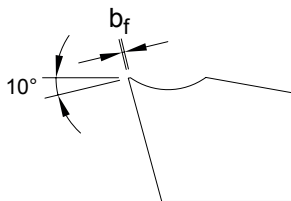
Neutrale openingshoek voor afwerking en voorbereiking
